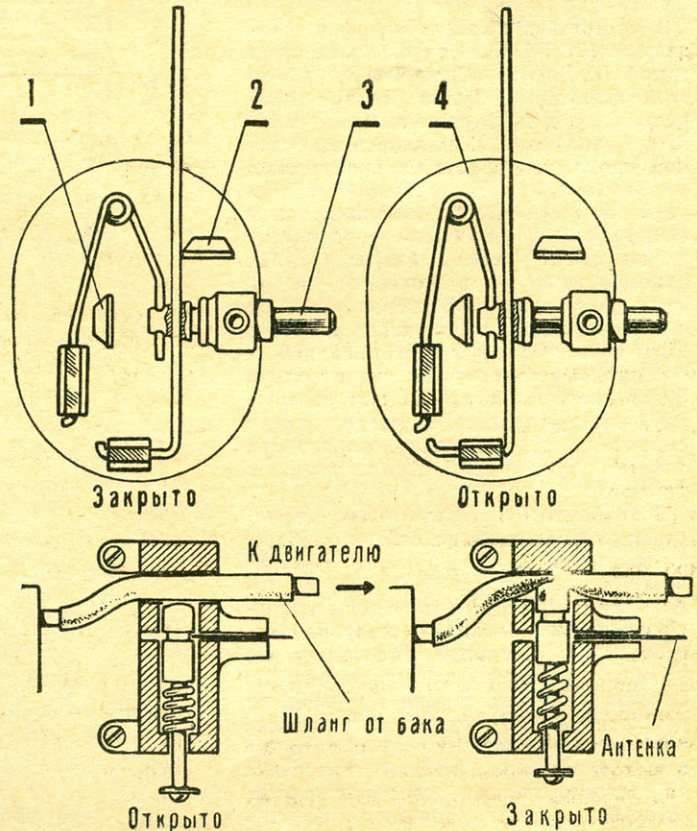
Остановочное приспособление с «пережимом» шланга.
